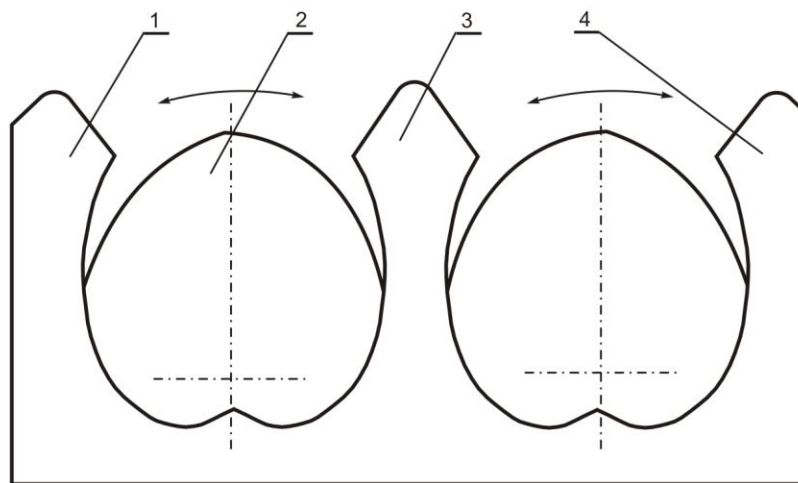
Плоско-коливальний робочий орган обрізувача дерев
